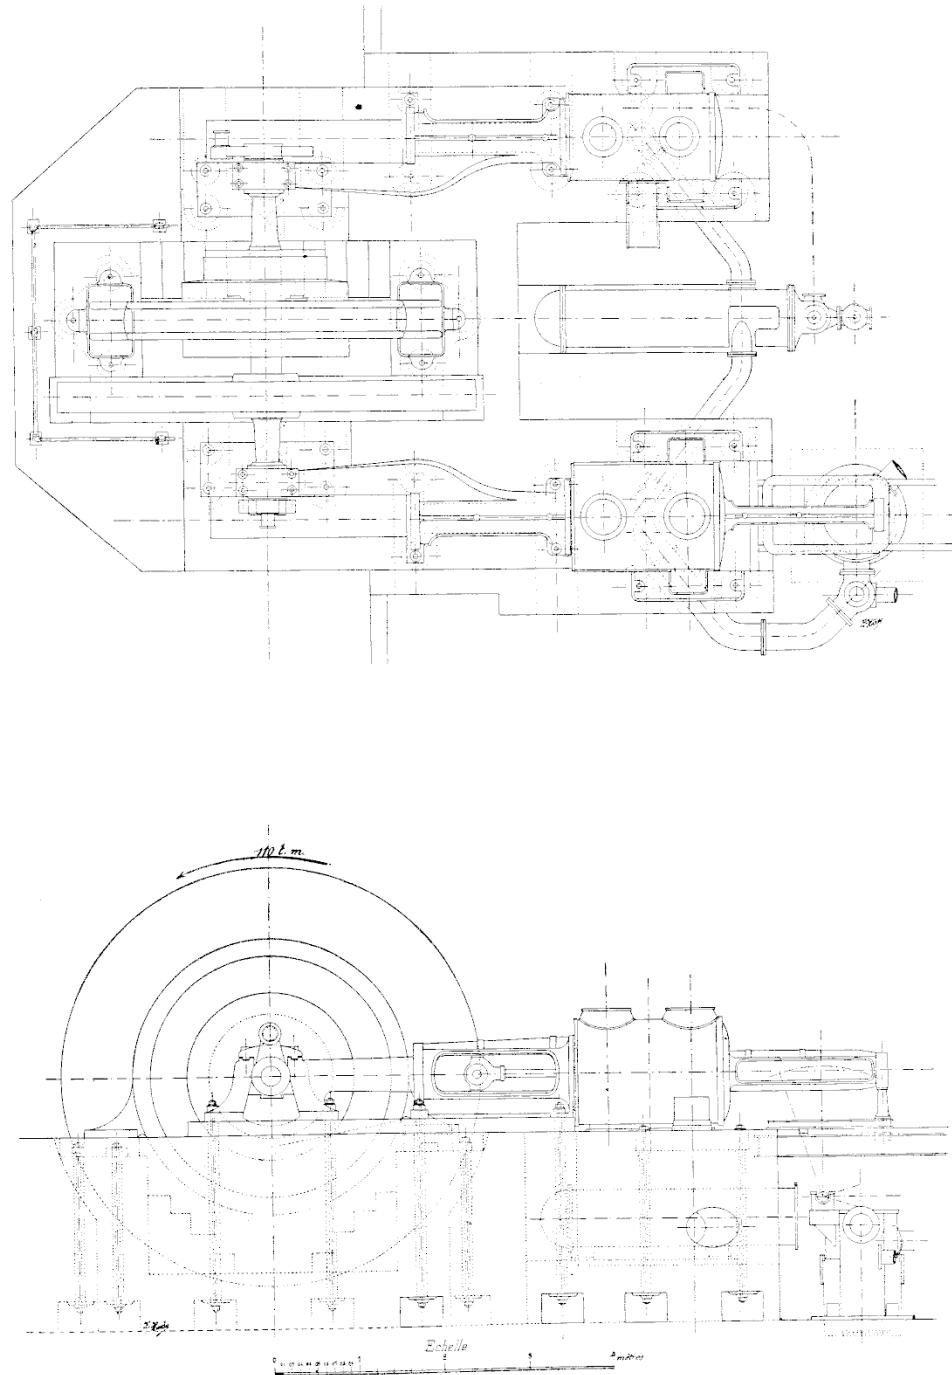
Groupe électrogène à courant continu "Elektrotechnische Industrie" — Stork frères.
